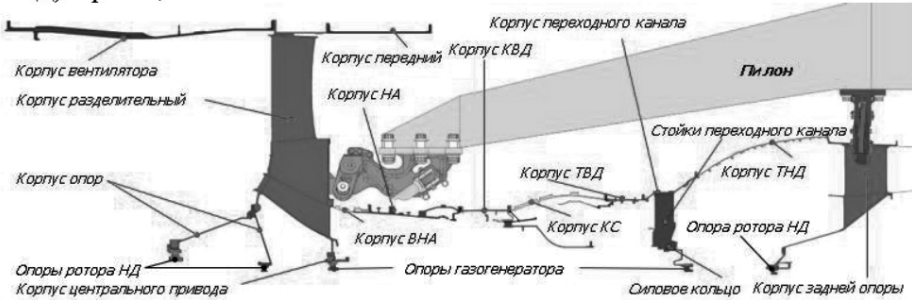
Силовая схема статора и подвеска двигателя к ВС
